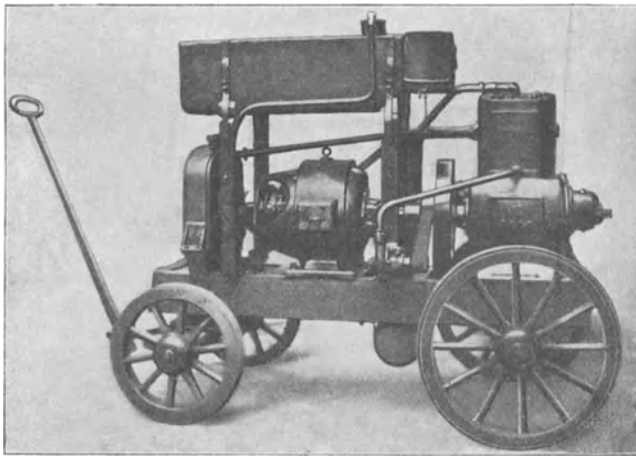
Fahrbarer Gleichstromschweißumformer mit Benzolmotorantrieb.
